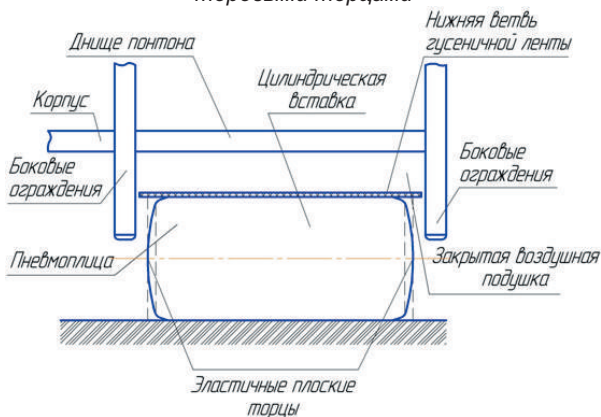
Схема продольного сечения пневмоплиты с плоскими торцами
